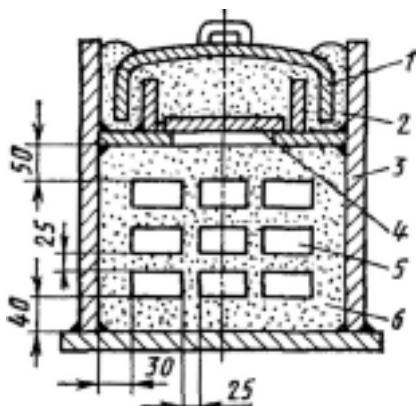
Ящик с песочным затвором для термической обработки поковок и деталей: 1 — крышка; 2 — песок; 3 — ящик; 4 — поддон; 5 — поковка; 6 — песок или древесный уголь
